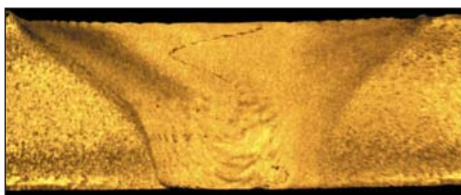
Макрошлиф поперечного сечения образца сварного шва из сплава АД0
